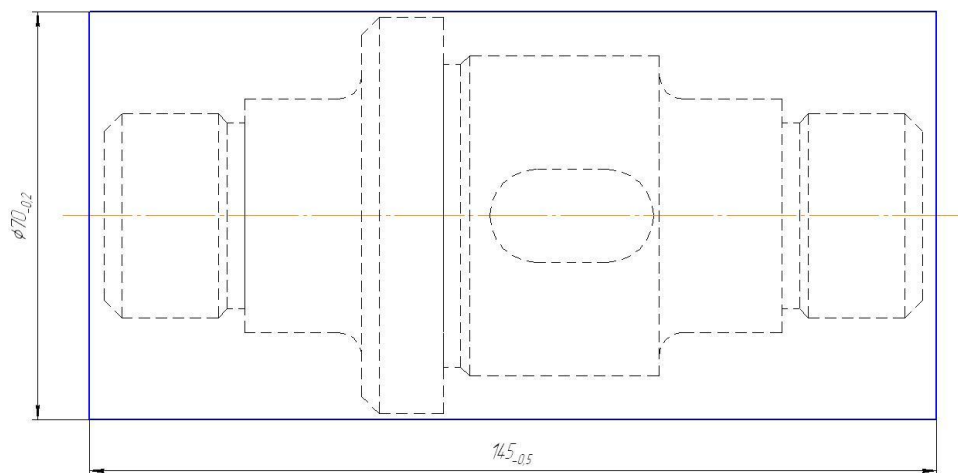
Ескіз штучної заготовки з прокату.
